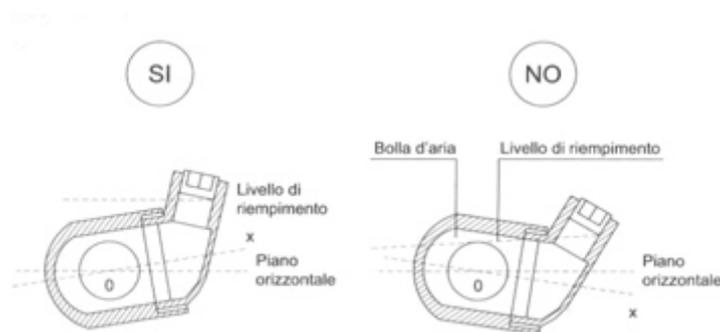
Raccordo di bloccaggio tipo GZ installato sul tubo orizzontale
